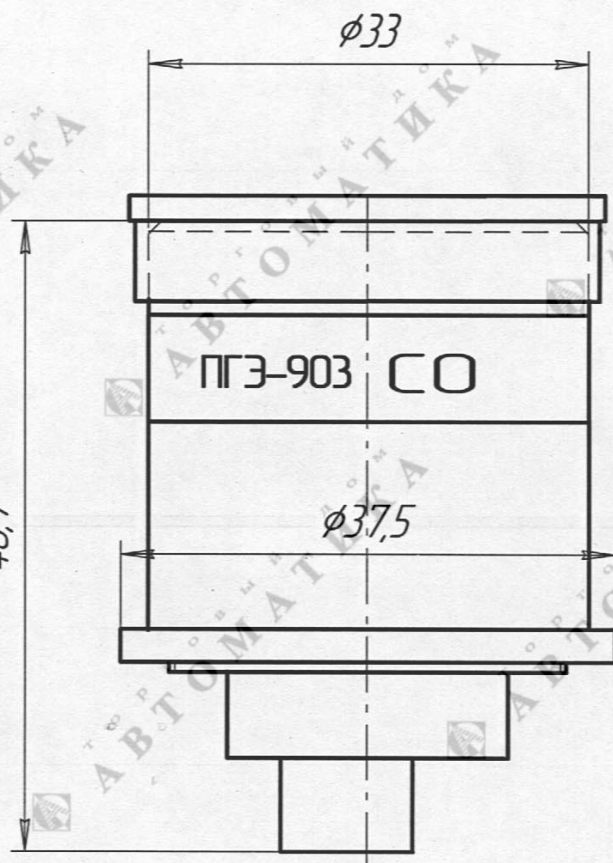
Общий вид преобразователя ПГЗ-903
